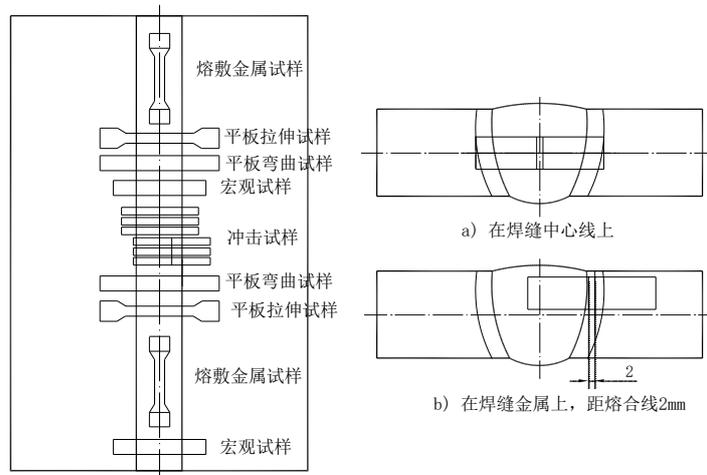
电渣焊或气电立焊对接焊试件的取样位置
